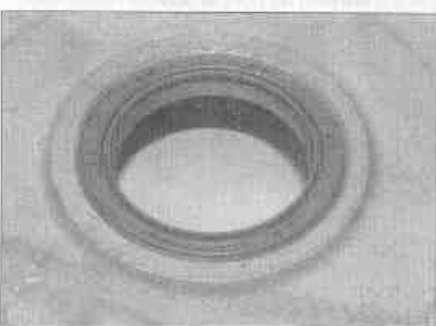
б. Внешняя кромка новой манжеты должна быть расположена заподлицо с крышкой газораспределительного механизма
